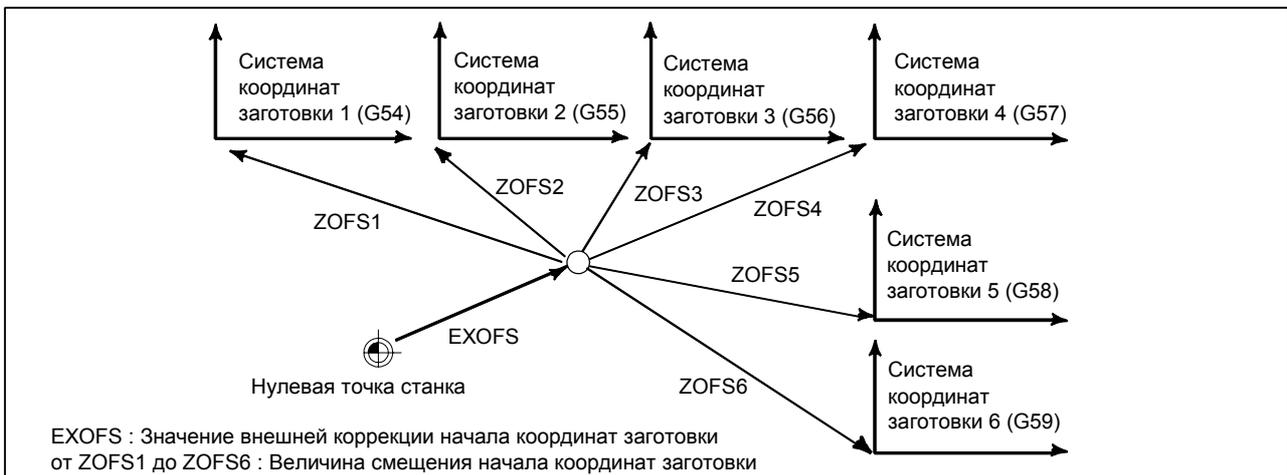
(а) Изменение величины внешней коррекции начала координат заготовки или величины коррекции начала координат заготовки
